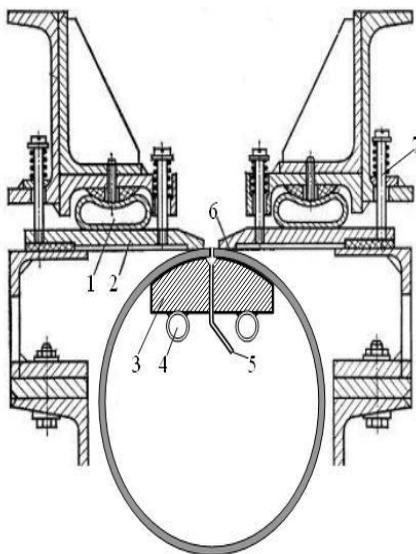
Стенд для сварки обечаек тонкостенных сосудов.
